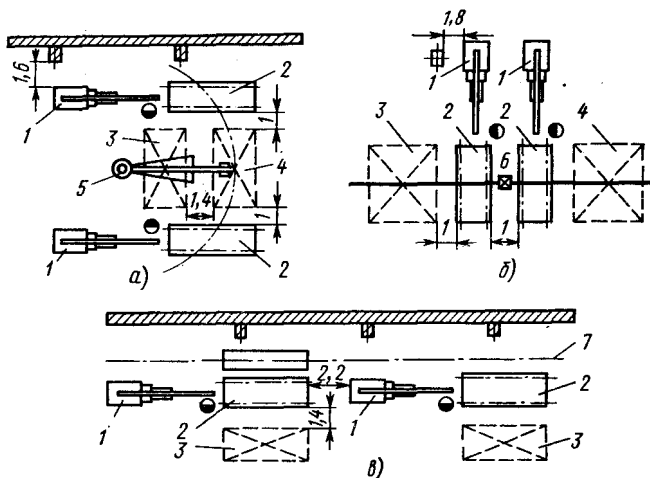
Варианты планировки рабочей зоны машин контактной сварки
